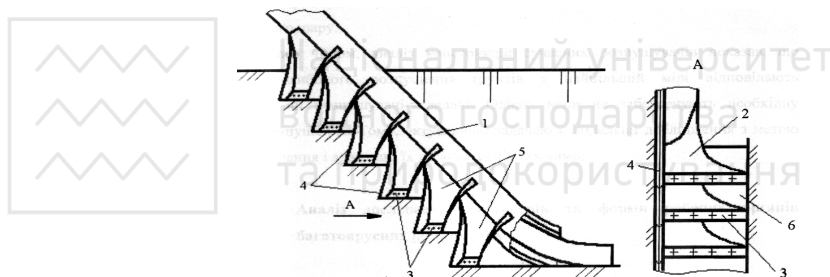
Загальний вигляд багатоярусного плужного одностороннього робочого органа: 1 – трубонапрямний тракт; 2 – підйомно-транспортуюча поверхня (полиця); 3 – підрізаючий ніж; 4 – розрізаючий ніж; 5 – прохідне вікно; 6 – довгомірний елемент
